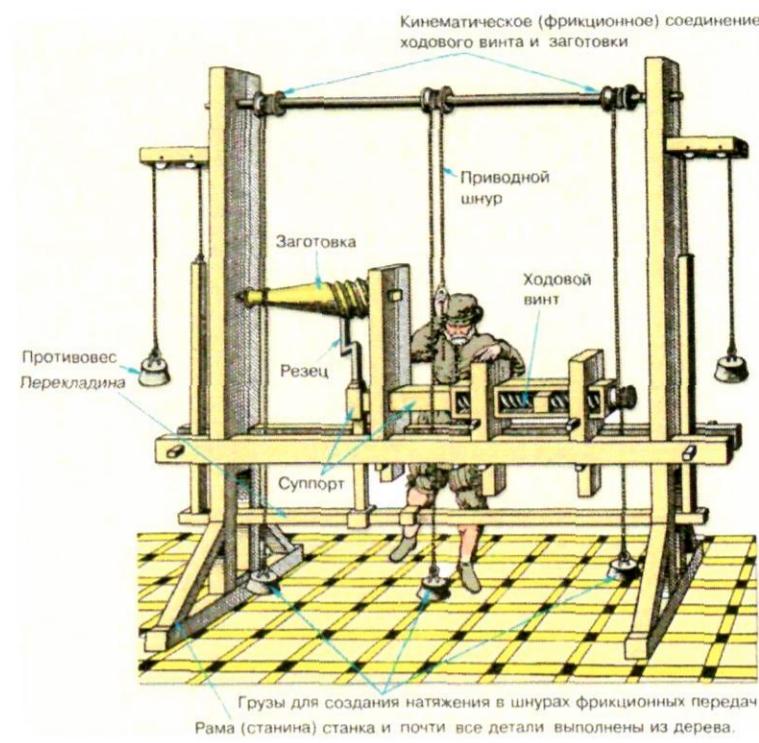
Токарно-винторезный станок Ж. Бессона
